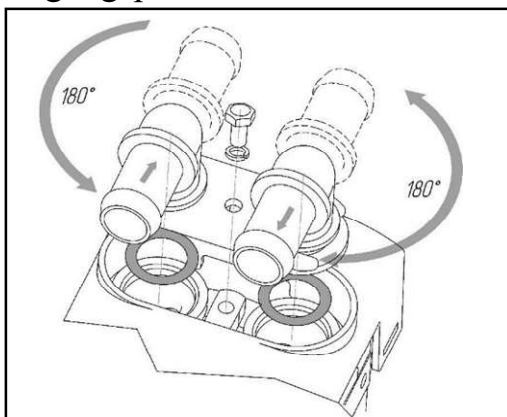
Winkelleitungsbefestigung für FLOW 5
